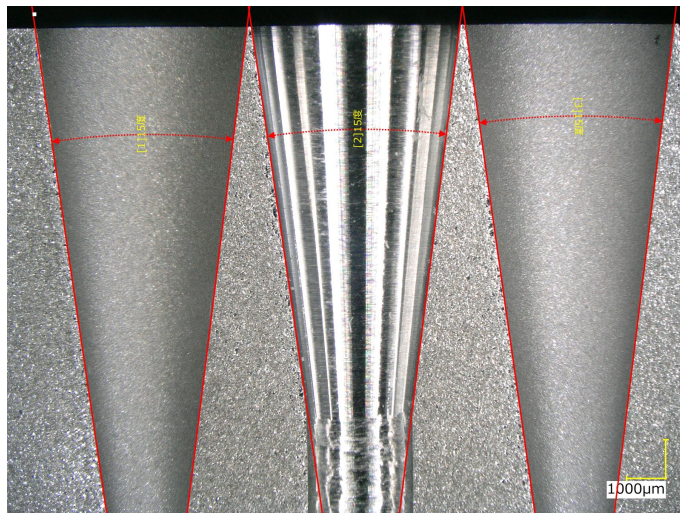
真中が切削加工の加工表面。左右がワイヤー放電加工の加工表面。
